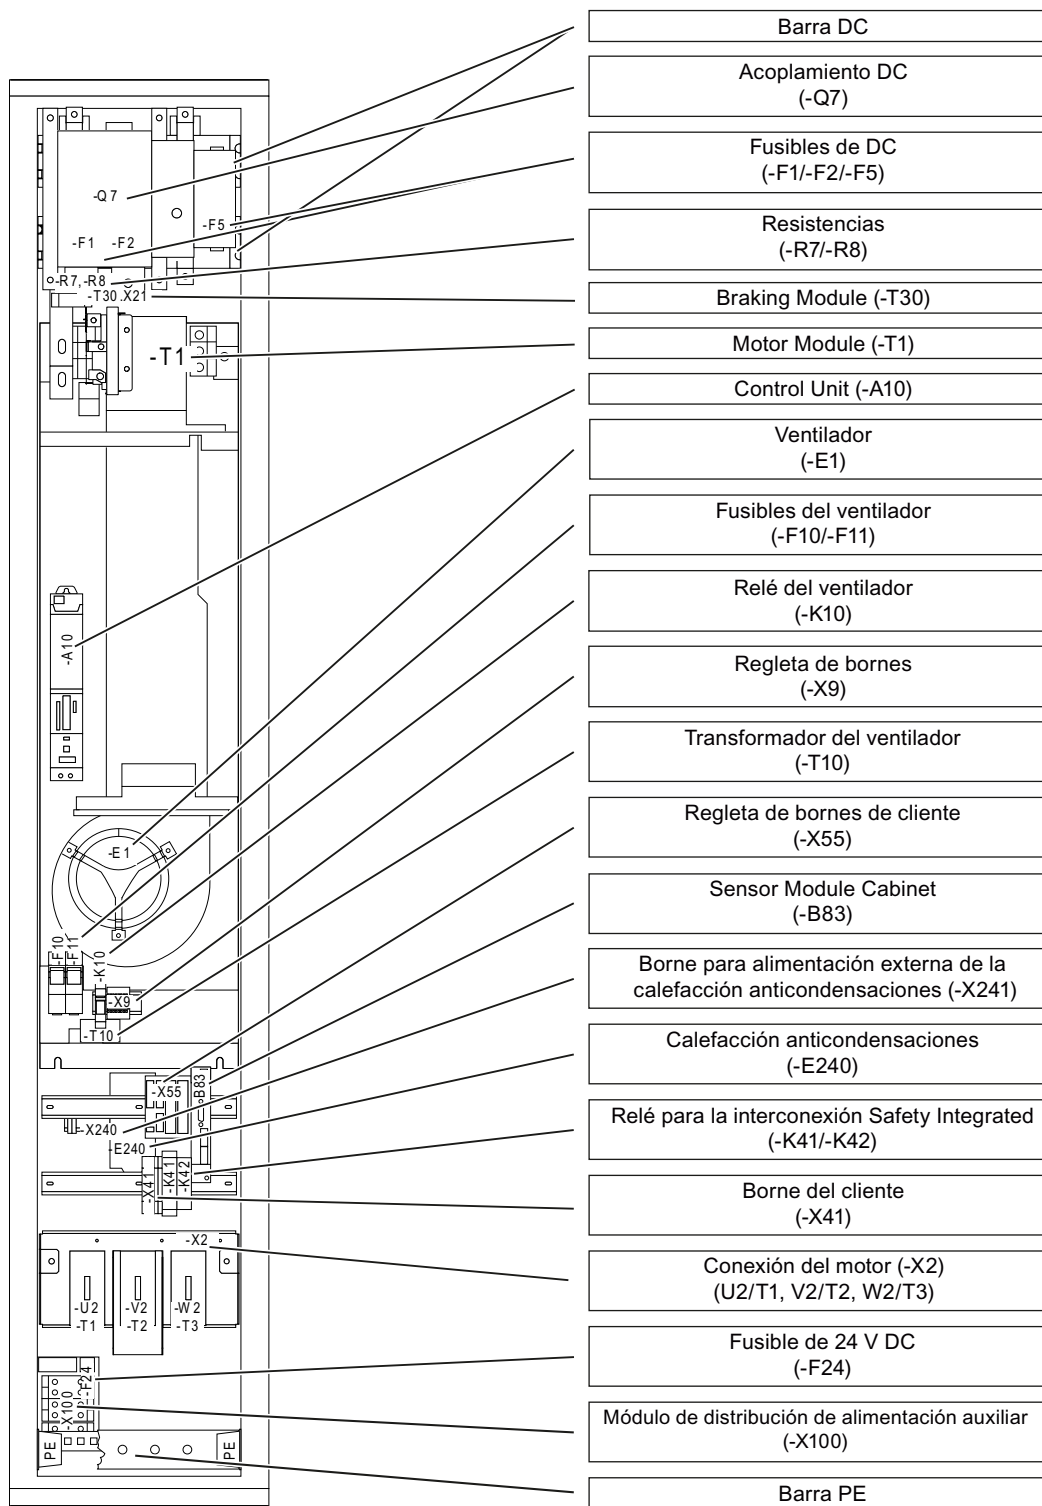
Diseño de Motor Module, diseño Chassis (tamaño FX)
